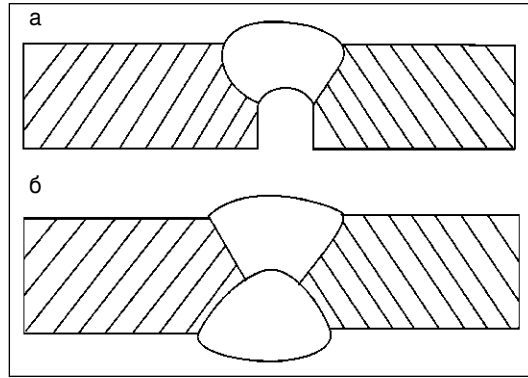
Выполнение стыковых швов ручной дуговой сваркой на металле толщиной до 12 мм без разделки кромок: а — расчистка корня шва после сварки с одной стороны; б — сварка обратной стороны шва
